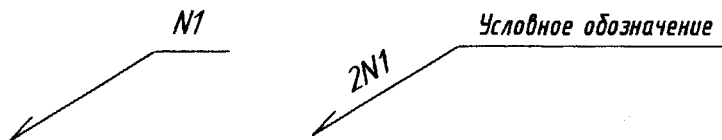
Обозначение одинаковых сварных швов на чертеже
